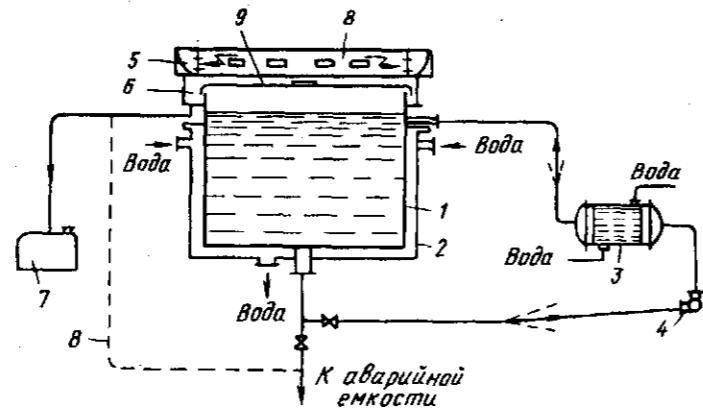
Схема охлаждения масляной закалочной ванны: 1 — корпус ванны; 2 — корпус (кожух) водяной рубашки; 3 — холодильник поверхностного типа; 4 — циркуляционный насос; 5 — короб вытяжной вентиляции; 6 — бортовые лотки; 7 — емкость для переливания масла; 8 — слив масла в аварийную емкость при отсутствии емкости 7; 9 — крышка ванны
